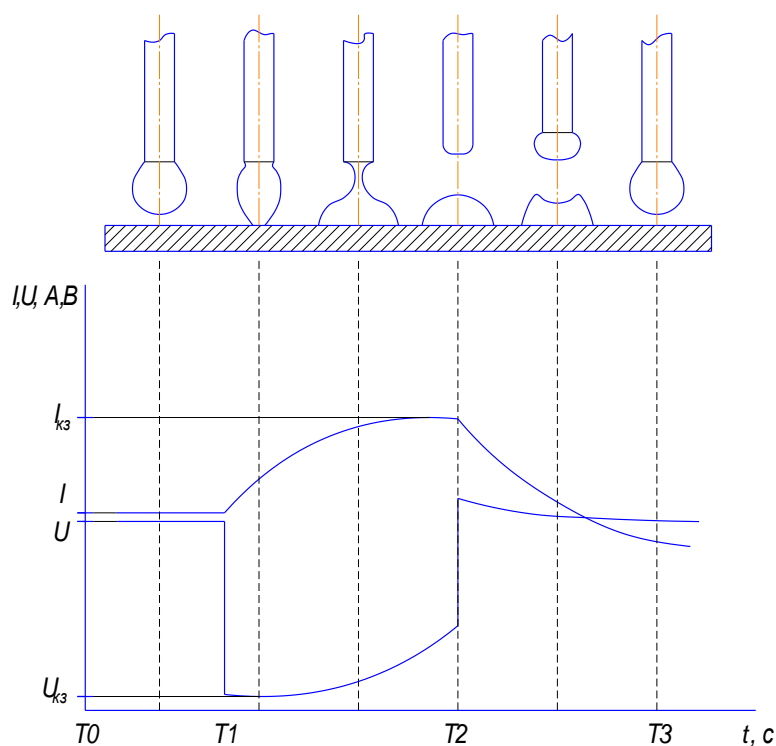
Типичные формы кривых сварочного тока и напряжения при традиционном способе полуавтоматической сварки [4]
